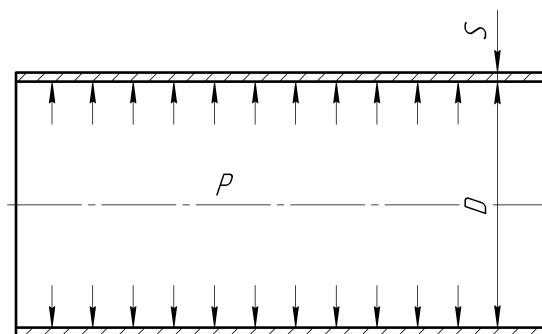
Розрахункова схема для визначення товщини стінки циліндричної обичайки
